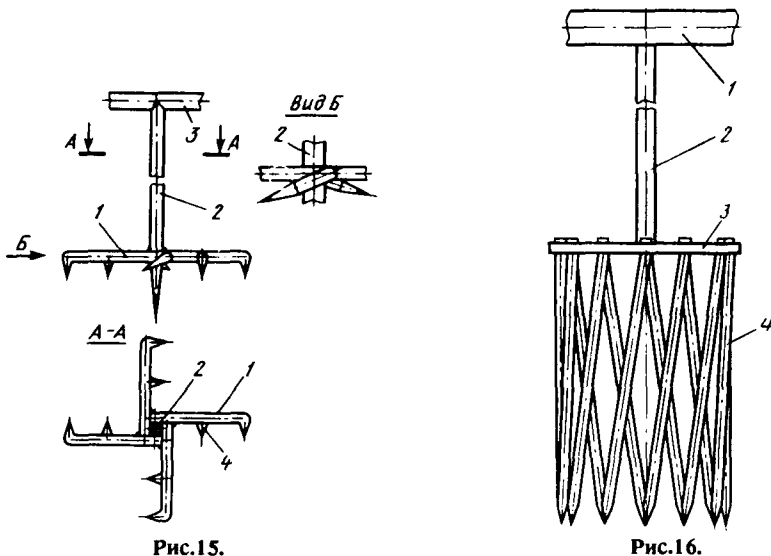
Четырехлучевой рыхлитель-захват для удаления сорняков мокрицы: 1 и 4 — изогнутый и дополнительный зубья; 2 — стержень; 3 — рукоятка
